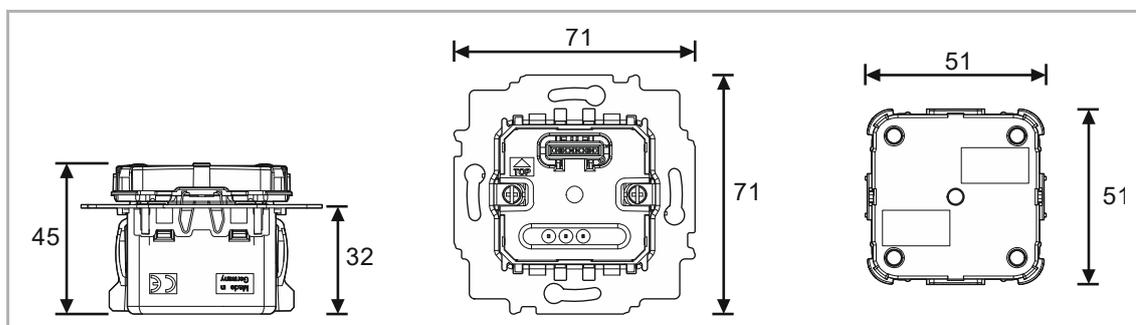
Dimensioni (misure indicate in mm) di tutti i tipi di apparecchi descritti
